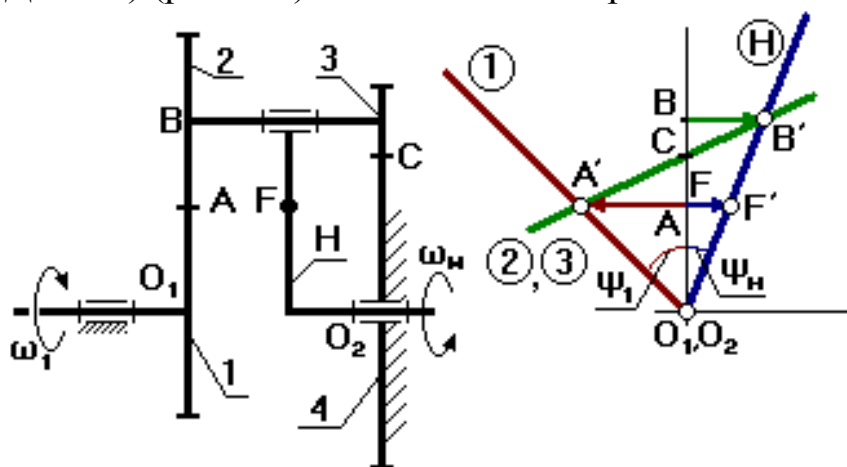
Редуктор Давида: 1, 2 – внешняя зубчатая пара; 3 – колесо; 4 – коронная шестерня; H – водило
